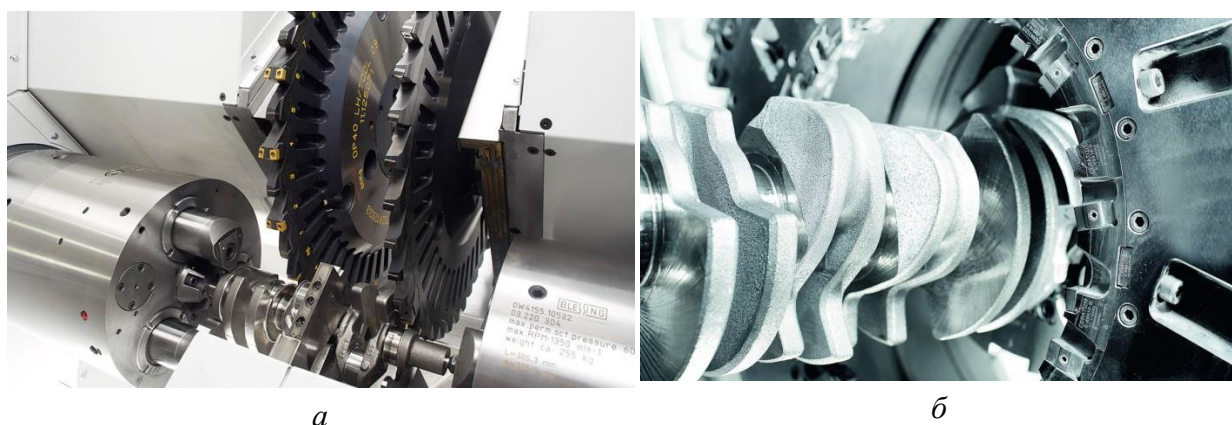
Фрезерування колінчастих валів фрезою з розташуванням пластин ззовні (а) та всередині (б) [14]
